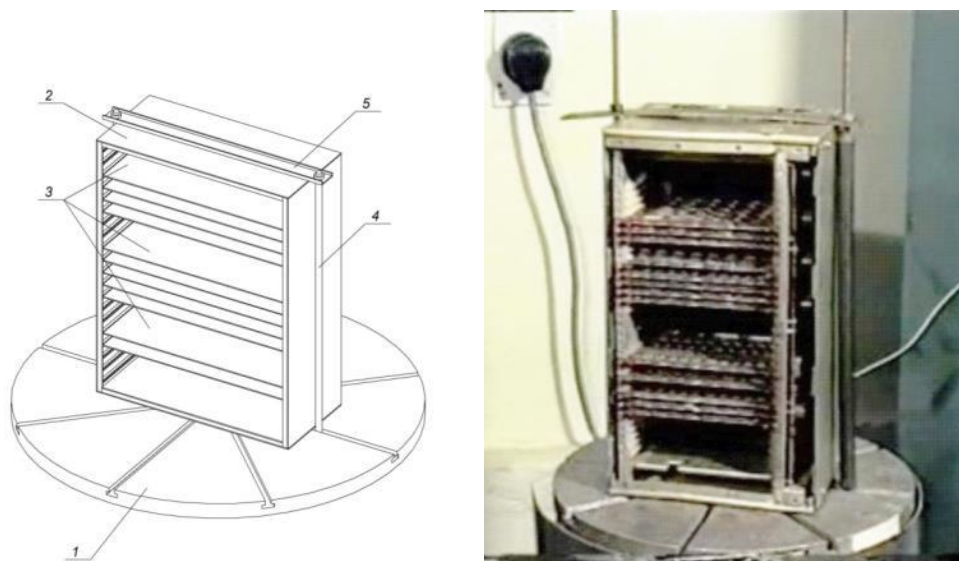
Схема кріплення блока ЕА на столі вібростенда: 1 – стіл вібростенда; 2 – блок ЕА; 3 – друковані плати; 4 – стійки кріплення; 5 – планка притискна
